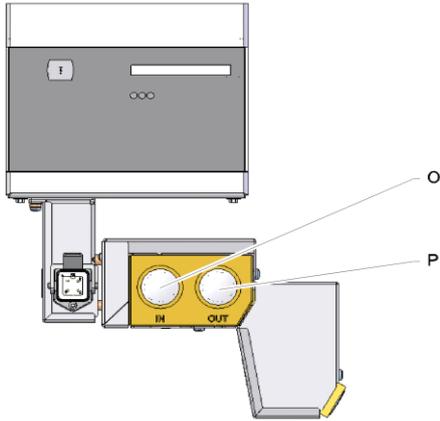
Соединительные разъемы конструкции "отдельно стоящий прибор"
